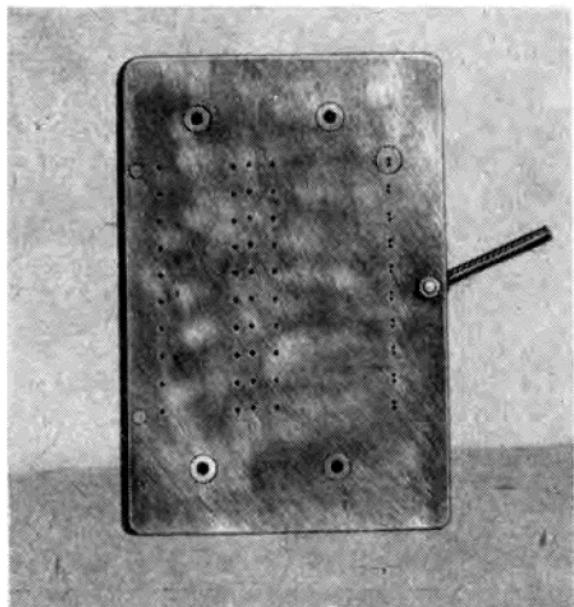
Bohrlehre zum Bohren der Tastenkontaktplatten nach Bild 10.11
